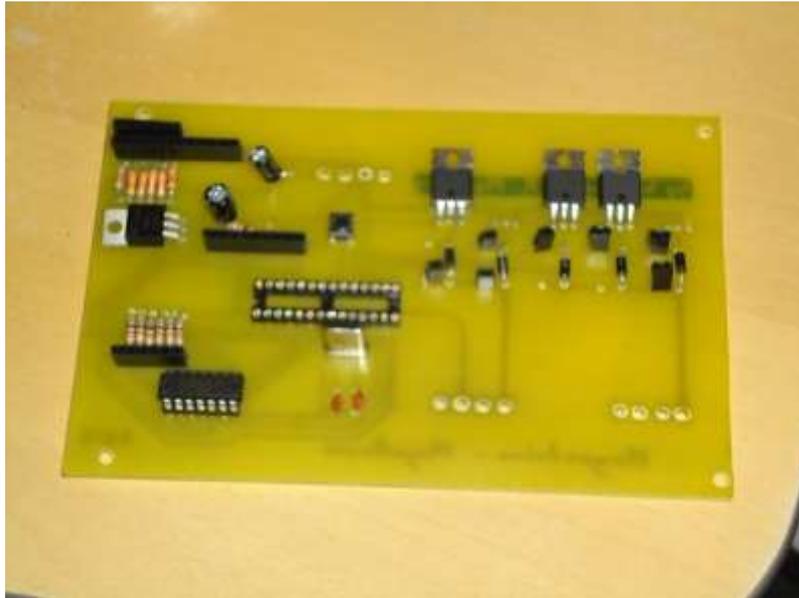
O Magneduino, com parte dos componentes já soldados
